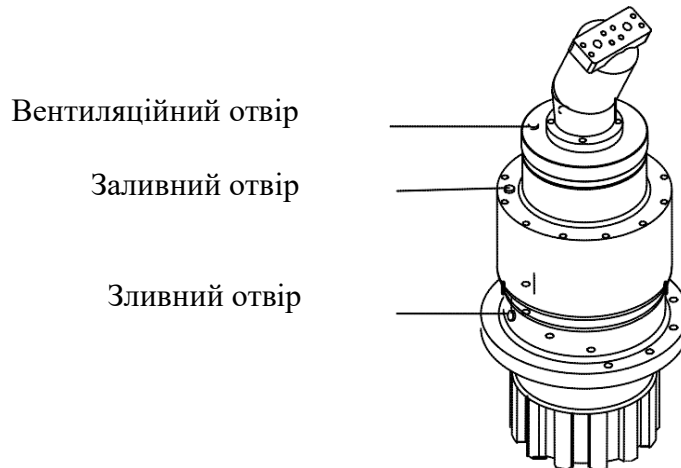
Заливний та зливний отвори редуктора лебідки
